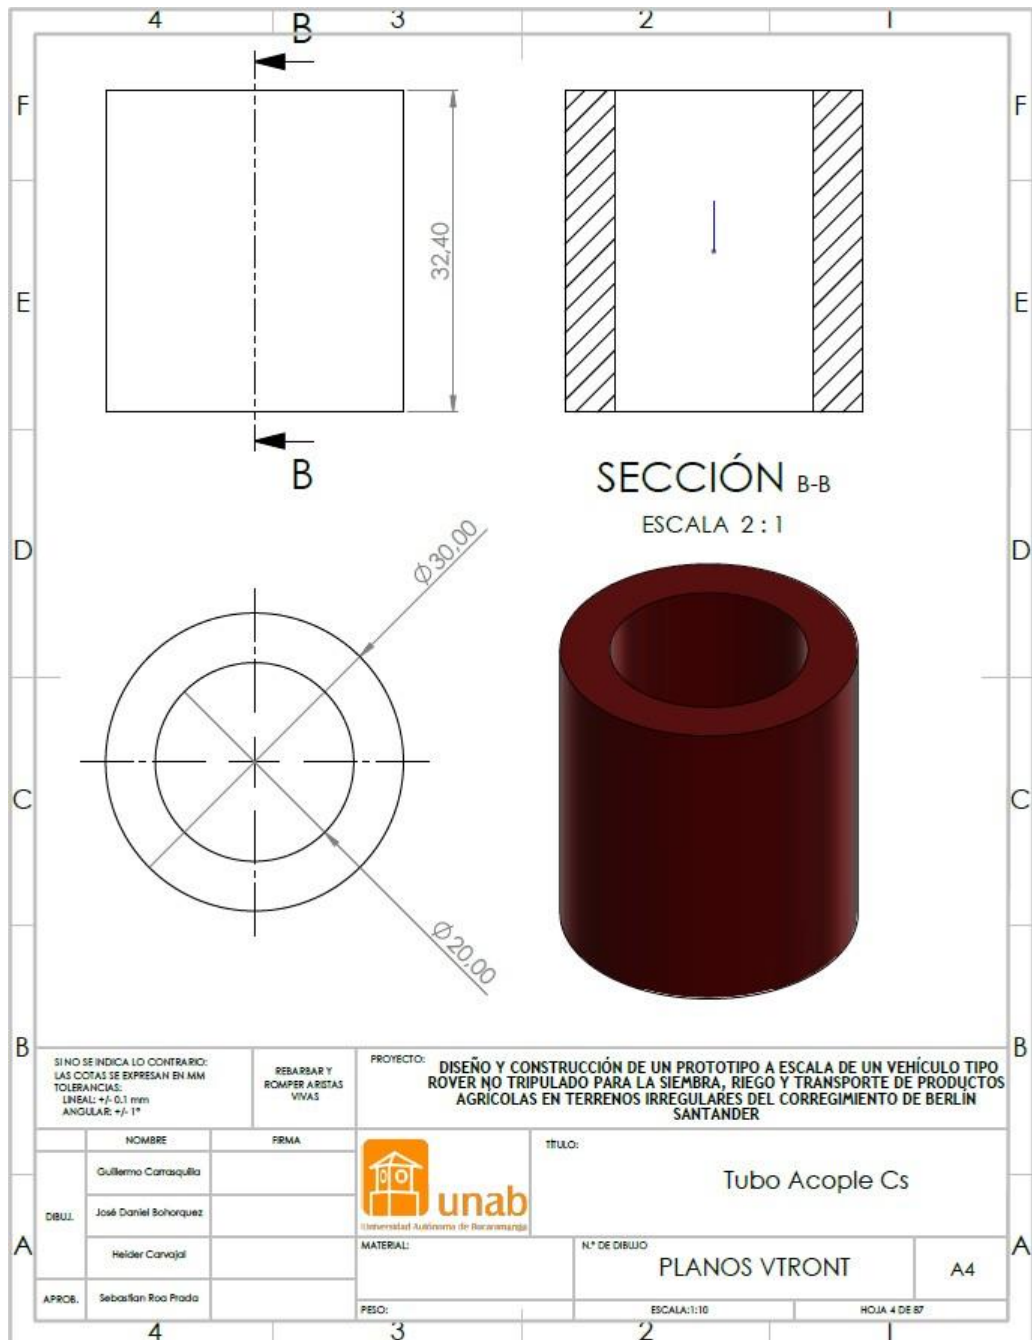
Plano de corte de tubería redonda para la camisa de las c's.
